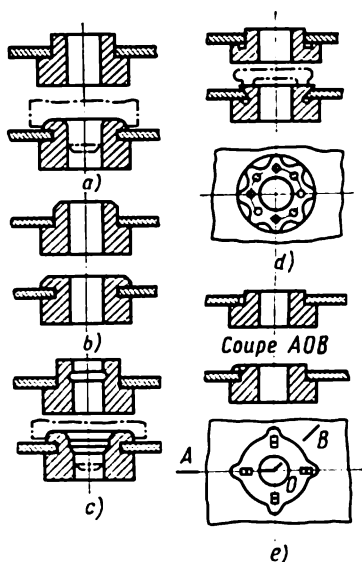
Assemblage de bagues exécutées sur des machines-outils avec des pièces tôlées
